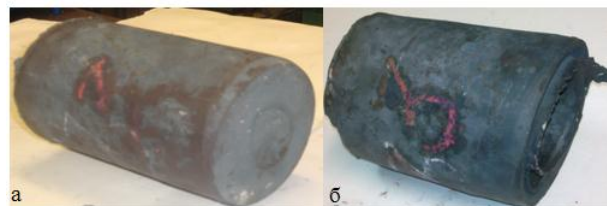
Фото задних концов обжатой заготовки и гильзы (заготовка с усеченным конусом и выпуклым торцом размером $L=40\pm 5$ мм с $R=250$ мм)
